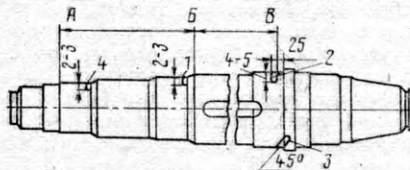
Контрольный образец для ультразвуковой проверки валов тяговых электродвигателей
